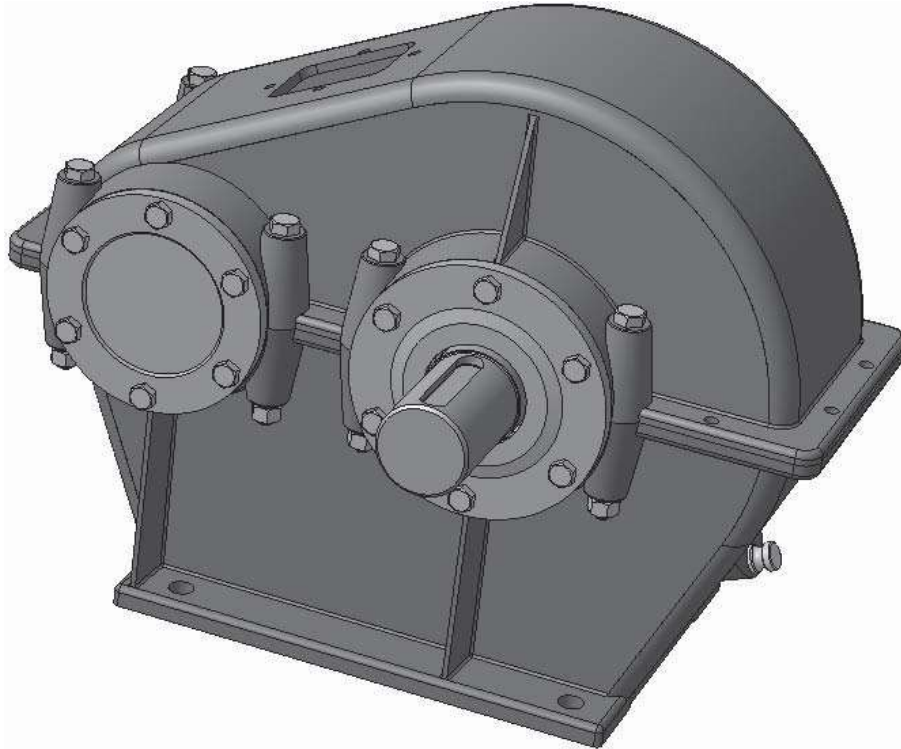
З'єднання болтами бобишок кришки і корпуса редуктора за допомогою команди *Масив по сітці
